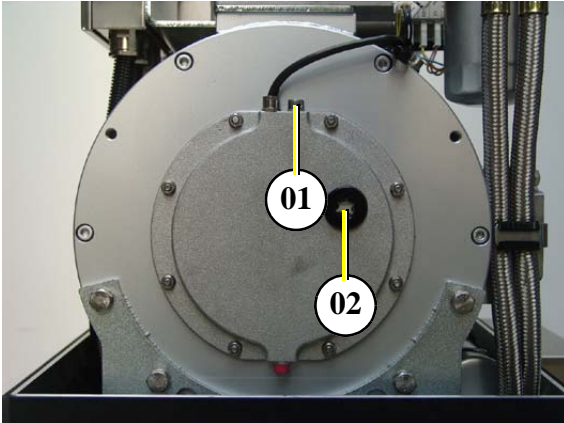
Werkzeug und Markierung entfernen
